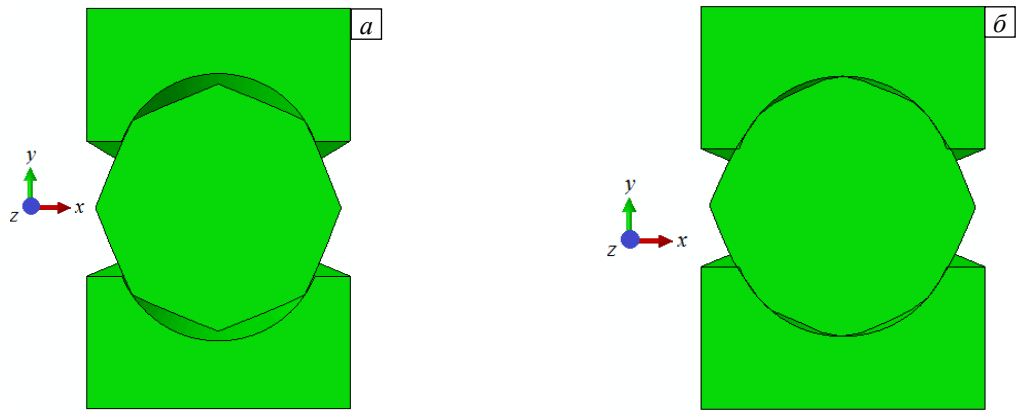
Начальный контакт заготовки и инструментов (а); контакт заготовки и инструментов в конце процесса прессования (б). Показано среднее (по оси z) поперечное сечение системы «заготовка–инструменты» (Рис. 6)
